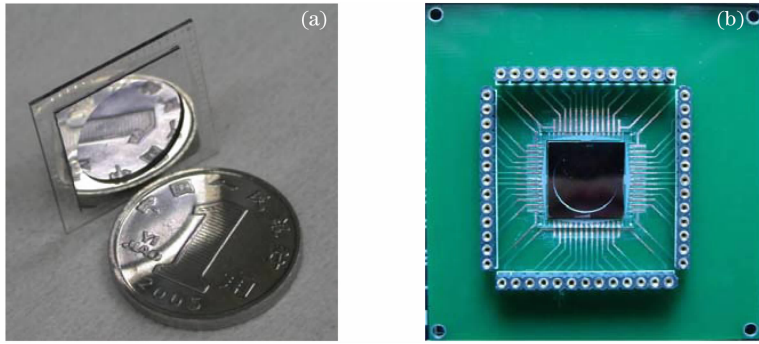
加工完成的微变形镜样件。(a)未打线;(b)打线到 PCB 板上
